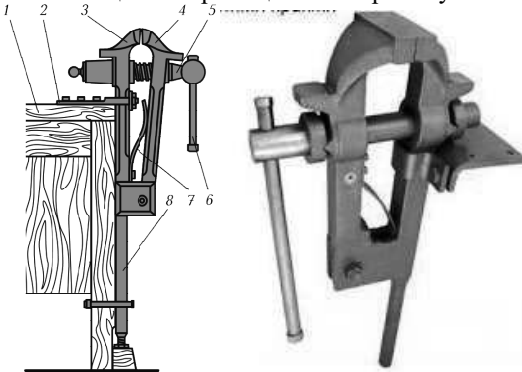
Стільцеві лещата: 1 – верстат; 2 – планка кріплення; 3 – нерухома губка; 4 – рухлива губка; 5 – затискний гвинт; 6 – рукоятка; 7 – плоска пружина; 8 – стрижень
